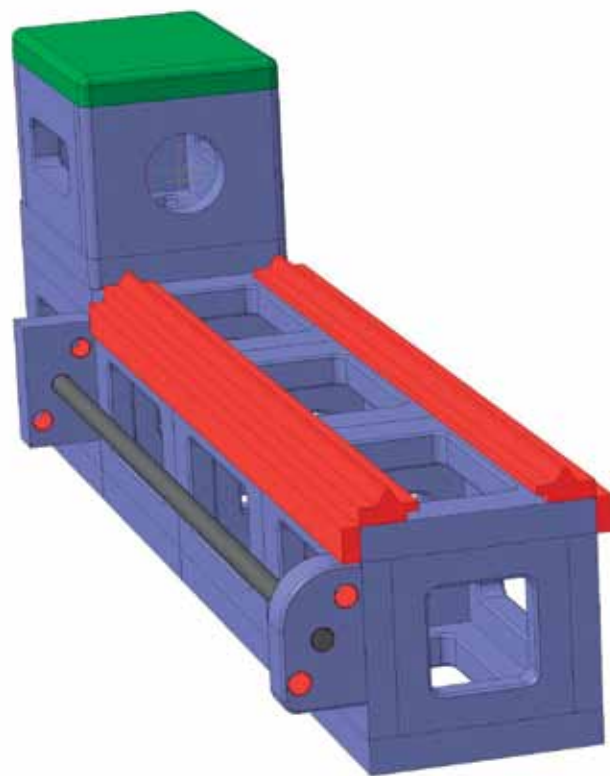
Корпус токарно-винторезного станка модели ТВ-6, выполненный из типовых элементов
